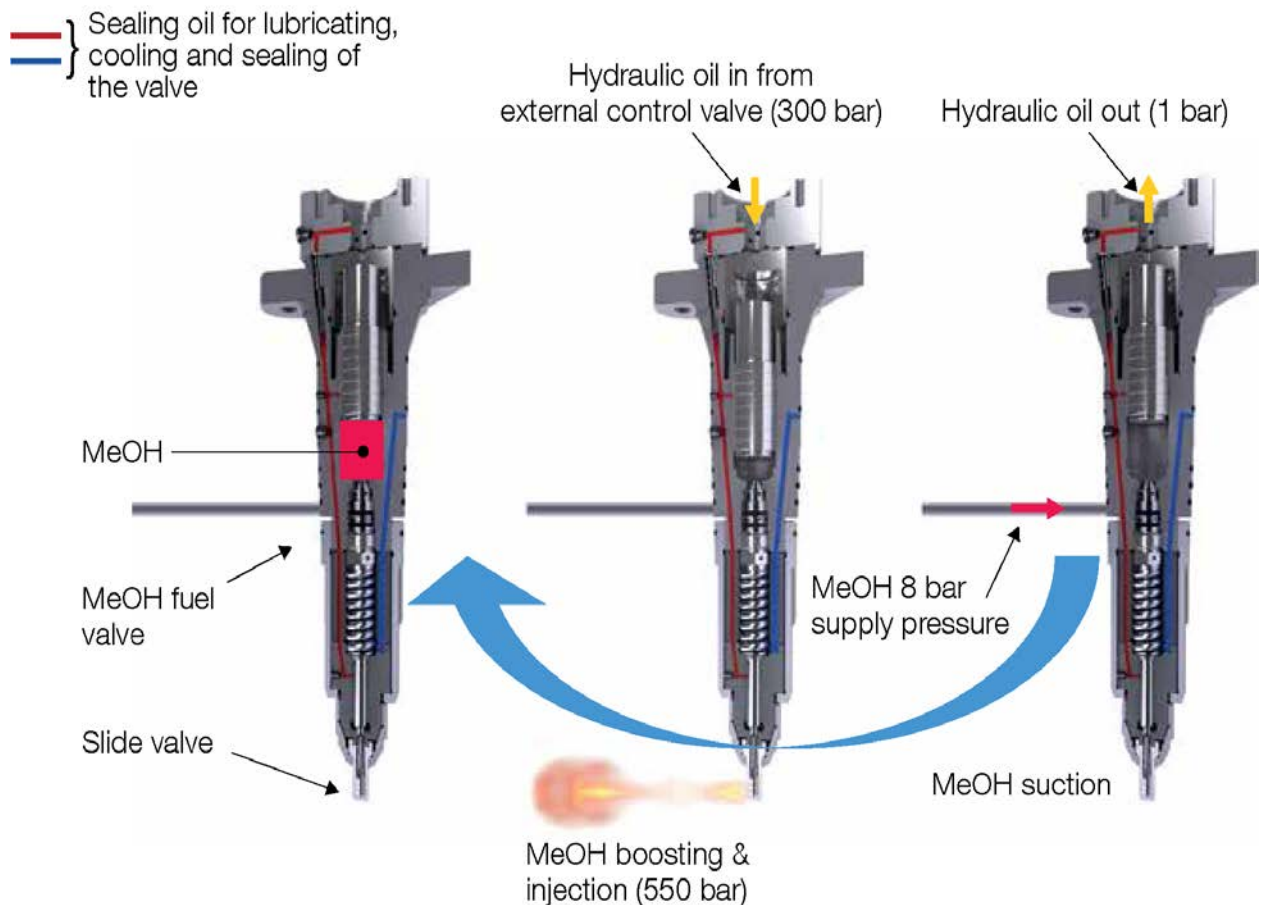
Принцип роботи паливної форсунки (BFIV) для метанолу
